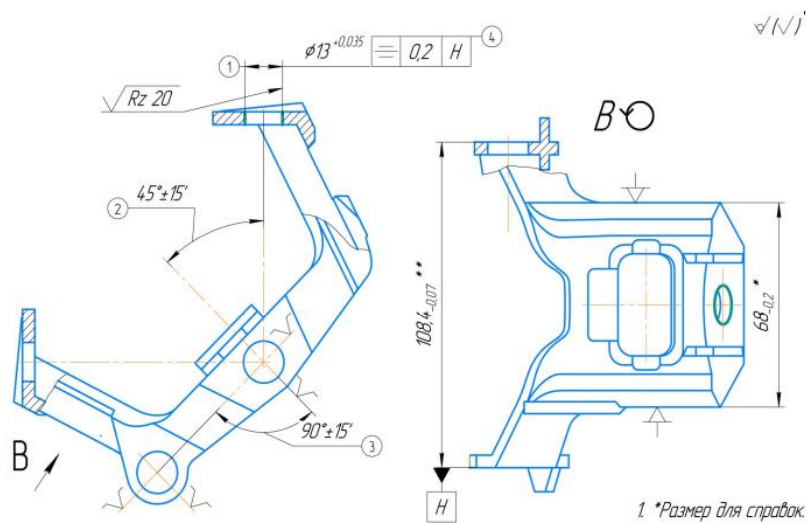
Эскиз к операции 095 – Фрезерная с ЧПУ
